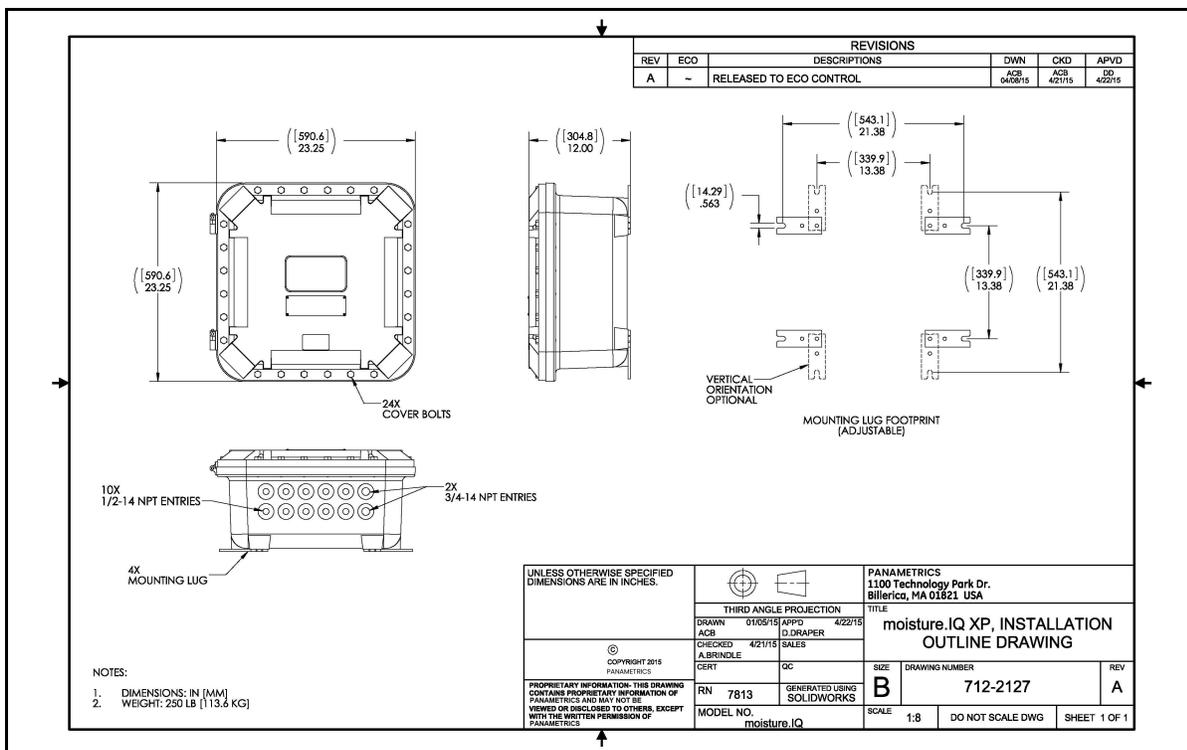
Umriss-Installationszeichnung für explosionsgeschützte Version (Zeichnung 712-2127_revA, Blatt 1 von 1)
